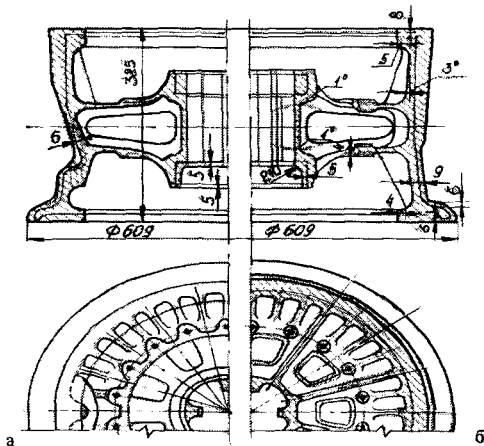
Припуски на механическую обработку в отливке барабана колеса: а – возможные, б – желательные
